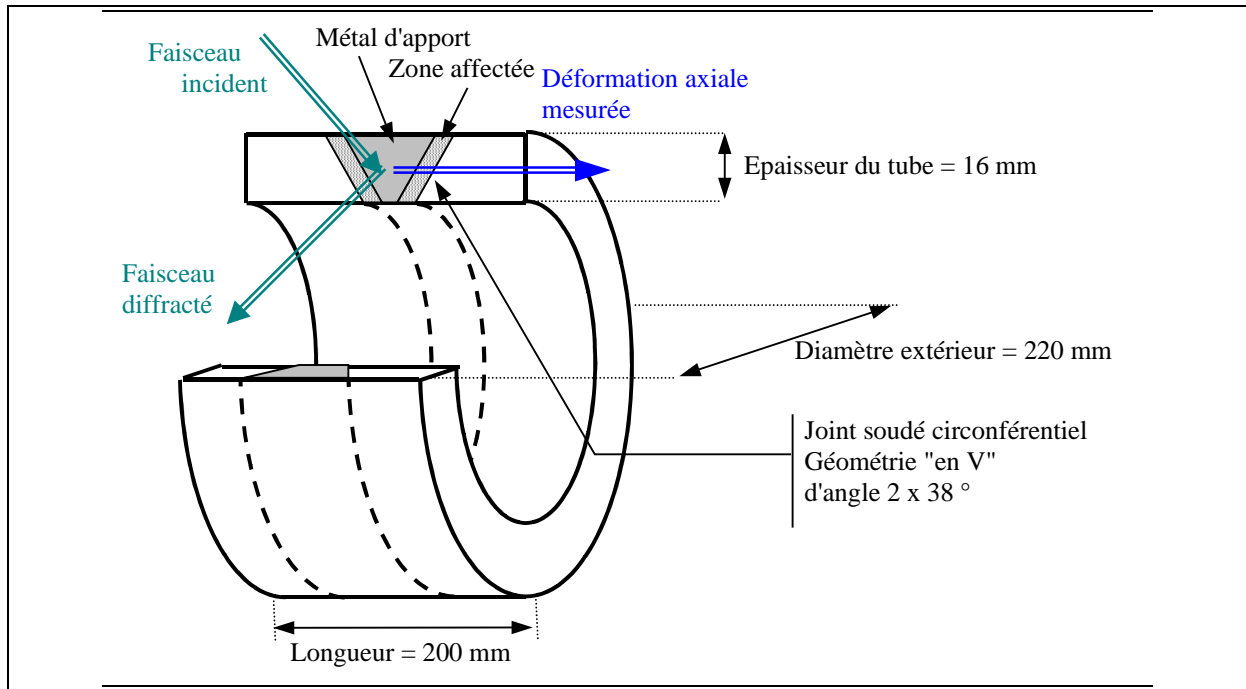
Vue en coupe du tube comportant un joint soudé, géométrie de l'échantillon et principe de la mesure.
